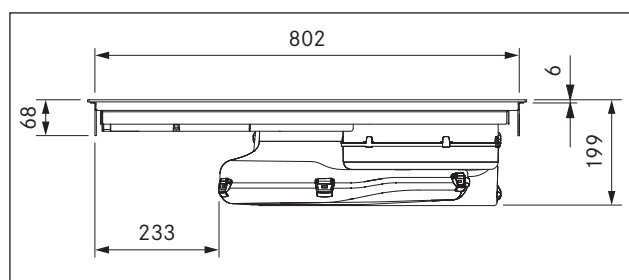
PUXU dimensioni apparecchio vista frontale
